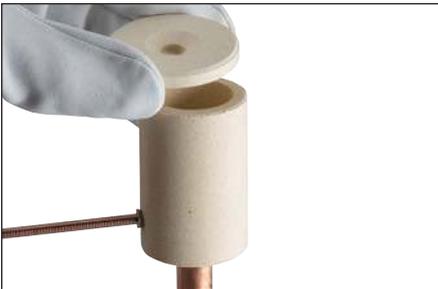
Placez le couvercle sur le dessus du Cadweld One Shot.
